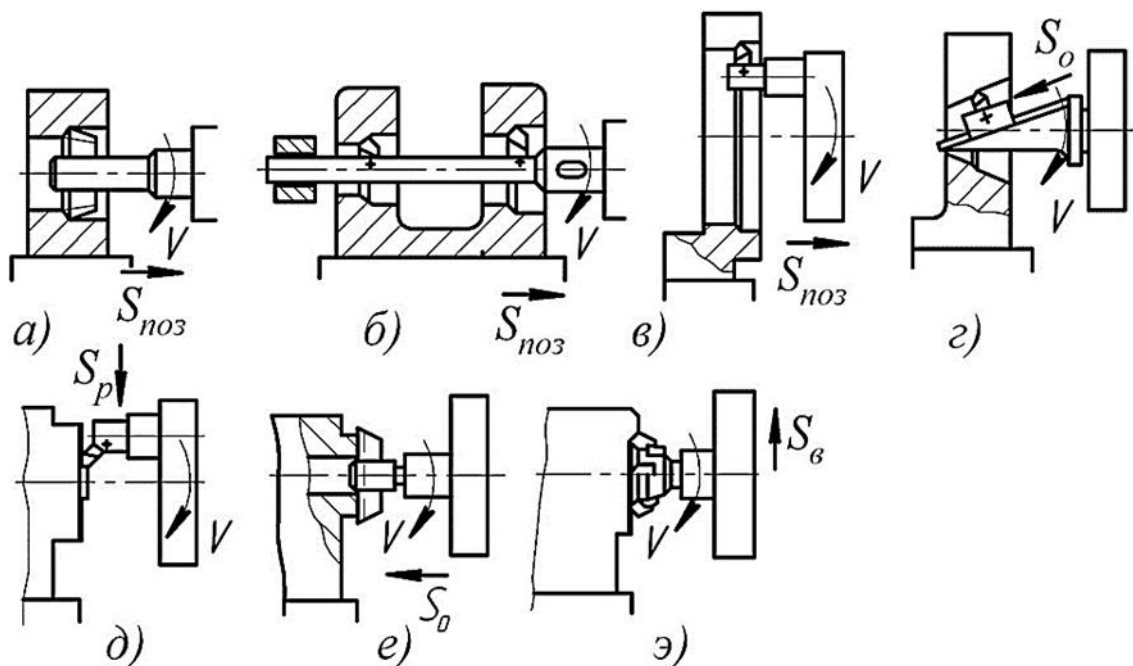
Схеми обробки заготовок на горизонтально-розточувальних верстатах
